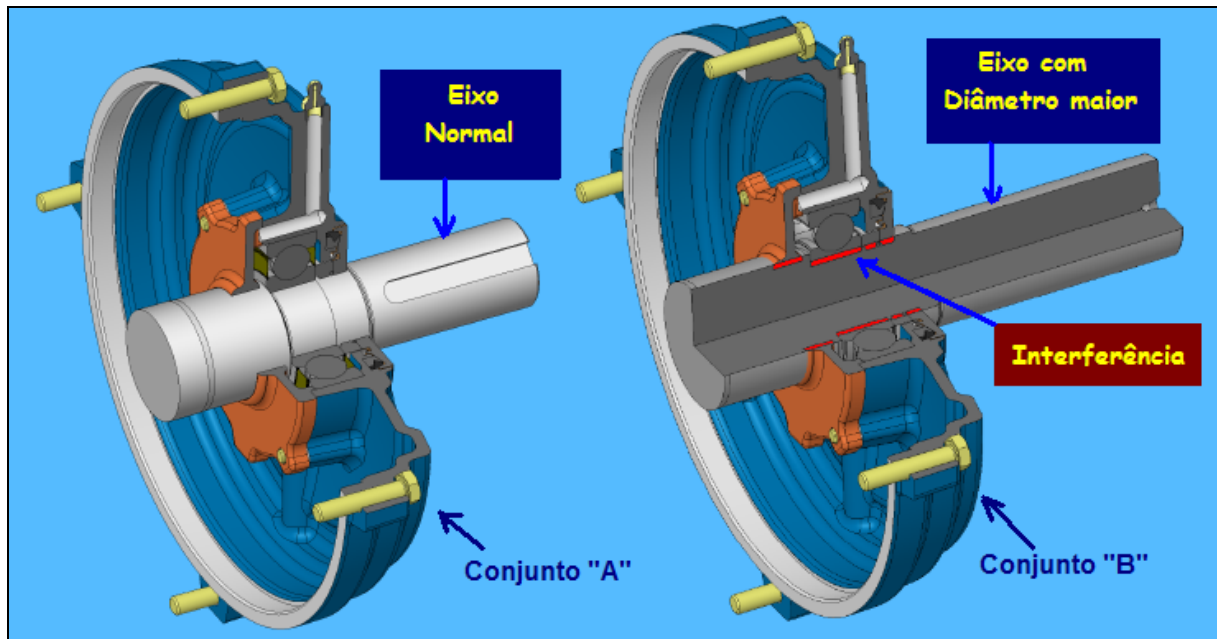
Exemplo de conjunto de mancal dianteiro de motor elétrico.
